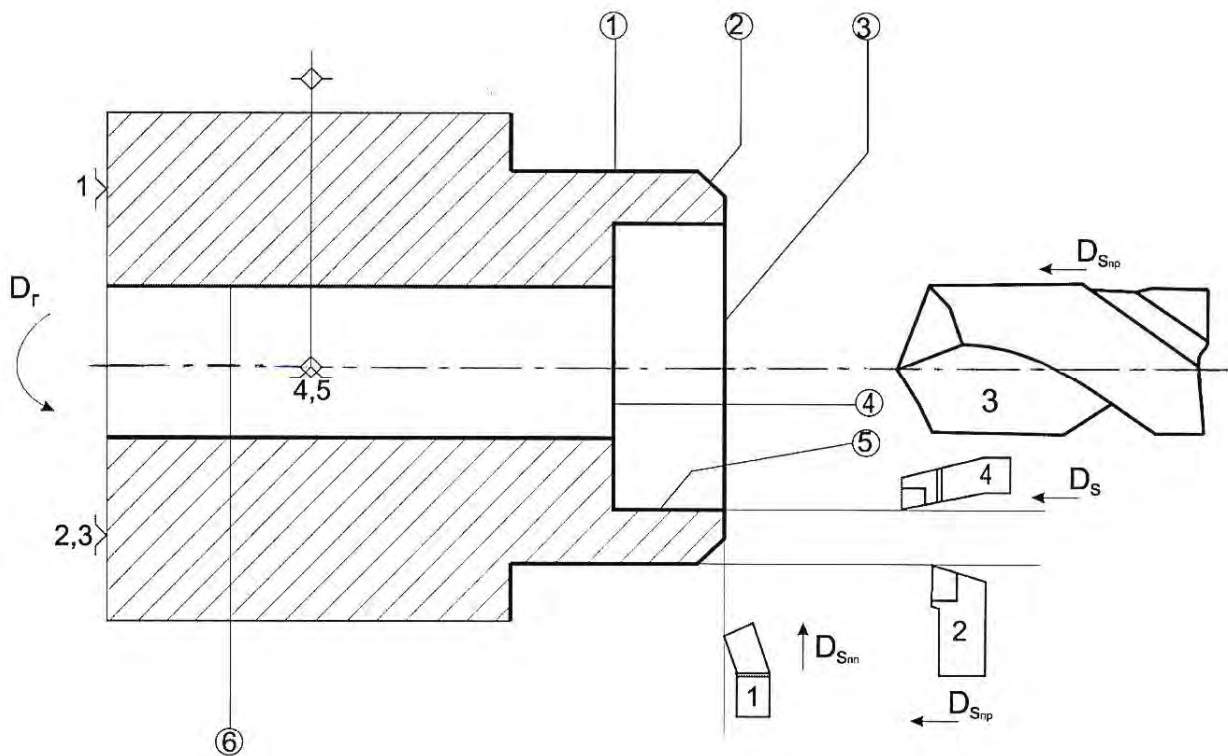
Эскиз обработки заготовки на токарно-винторезной операции
